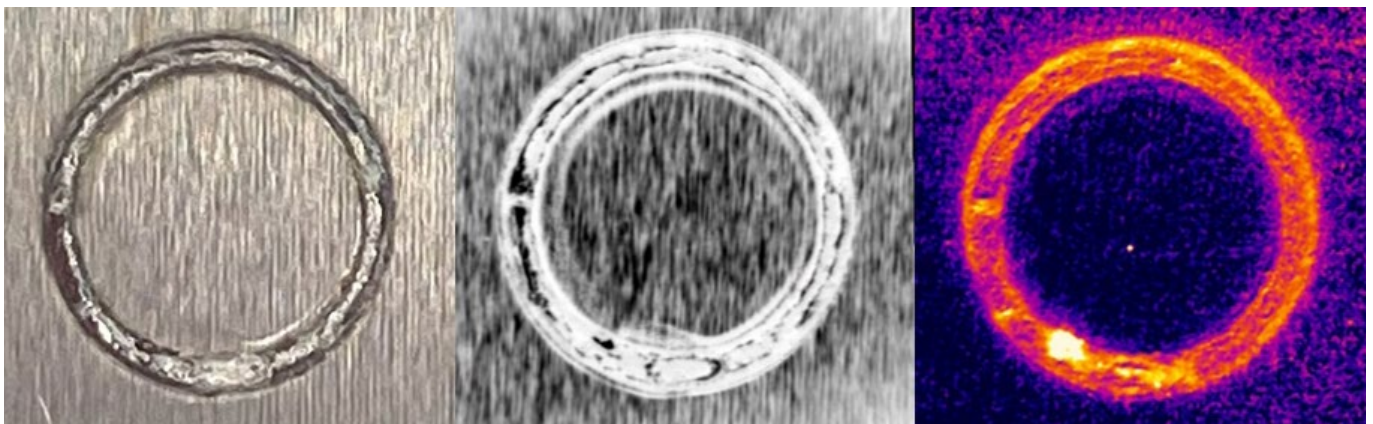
Bilder einer Aluminium-Stahl-Schweißnaht
